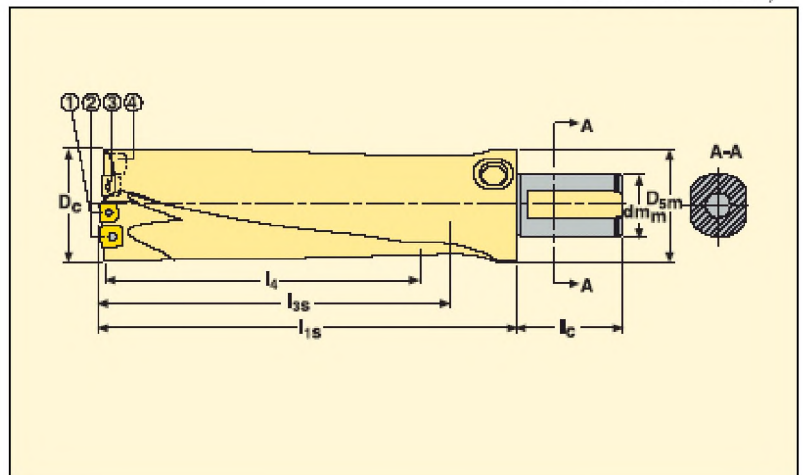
Свердло зі змінними твердосплавними пластинами
